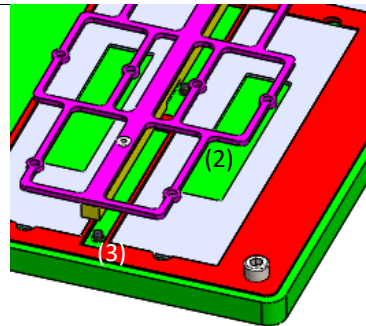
Gabarito para utilizar na soldadura laser robotizada
